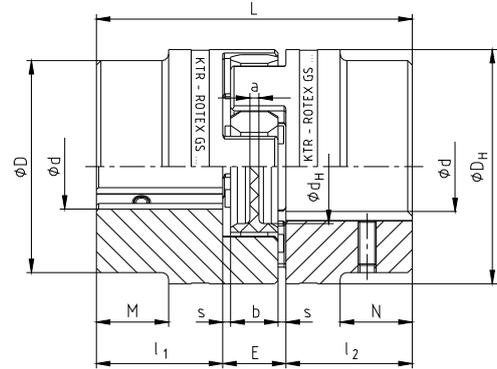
ROTEX® GS, типоразмеры 42 - 75
